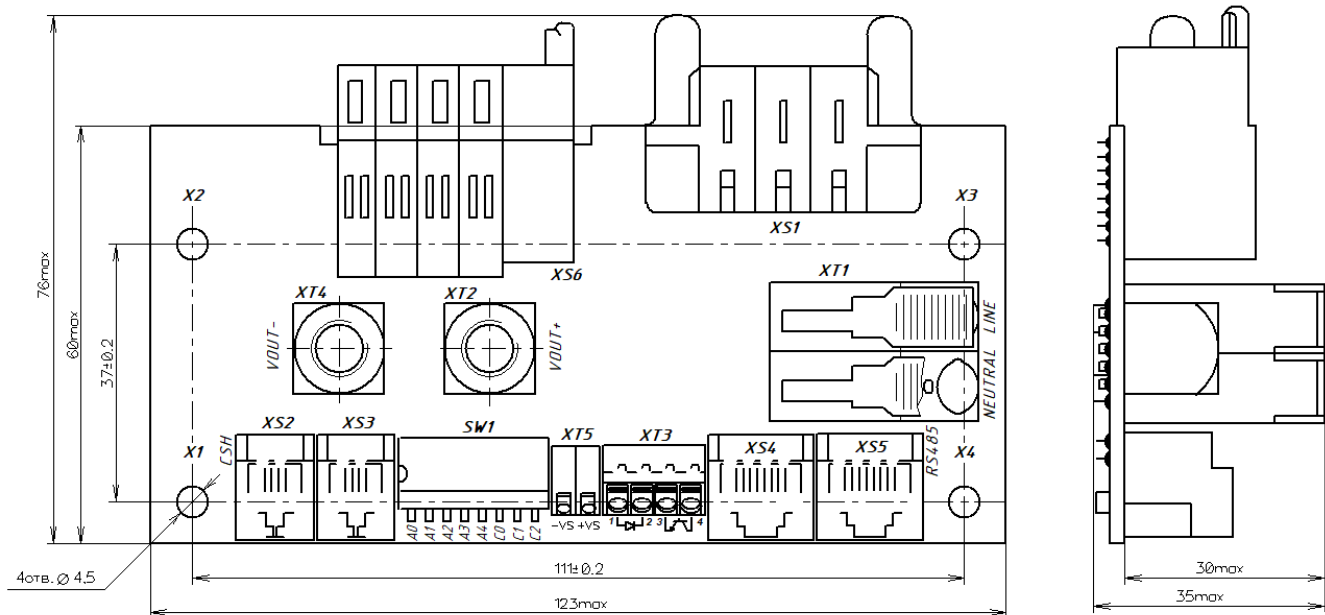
Габаритные размеры и расположение разъемов кросс-платы 1xKAN5000ЦХХ
